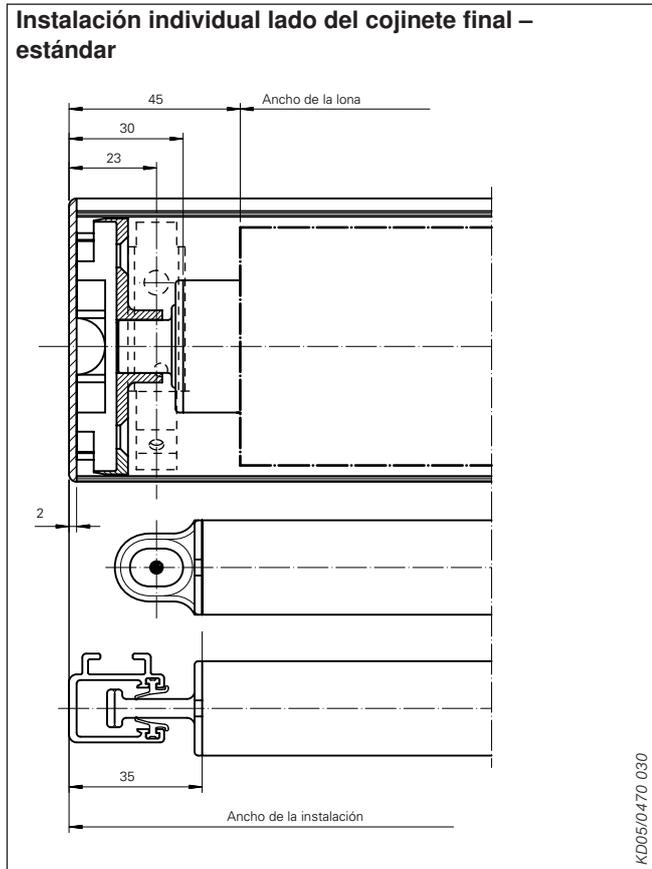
Situación de posición final instalación individual, lado del cojinete final
